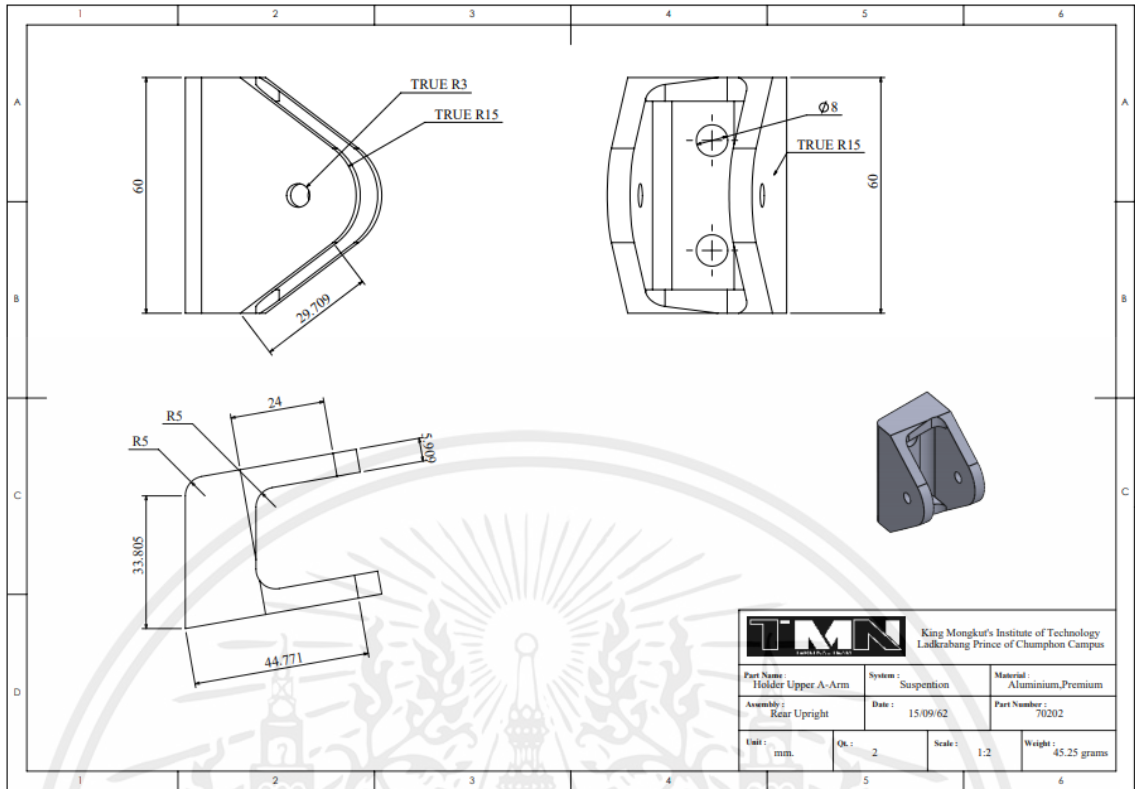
ส่วนประกอบของคอม้าหลัง (Rear Upright Assembly)
